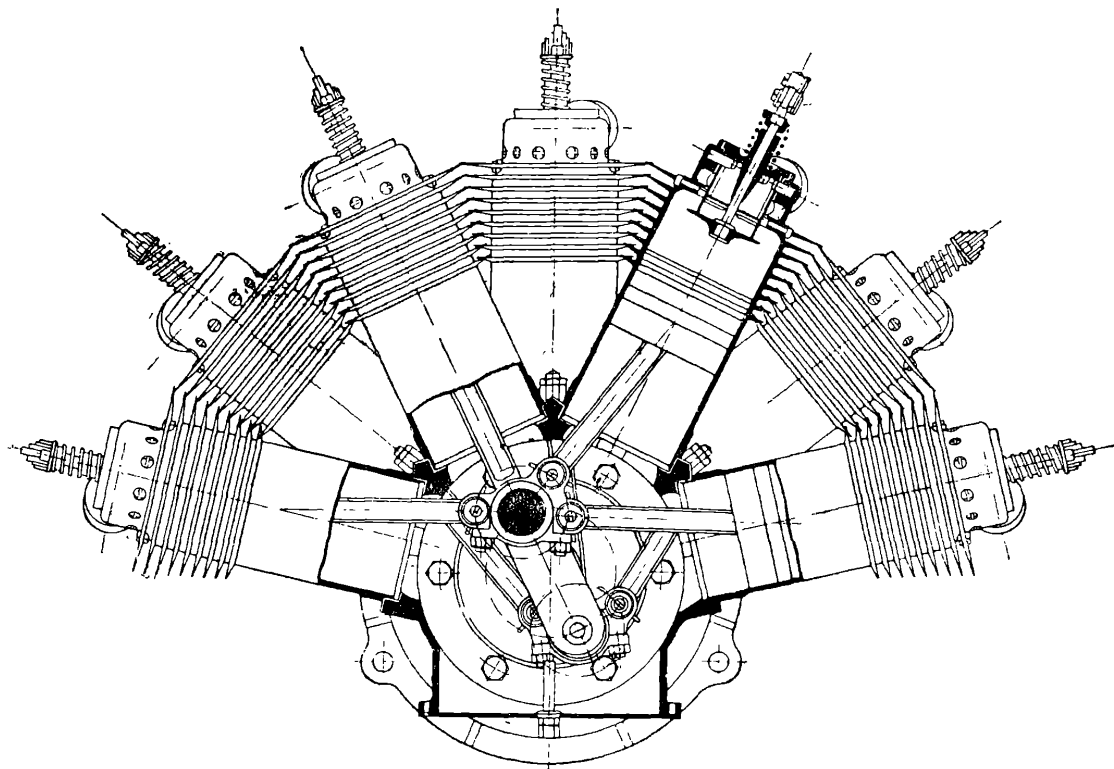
Пятицилиндровый веерообразный двигатель воздушного охлаждения PER конструкции Р. Э. Пельтри (поперечный разрез). 1905 г.
